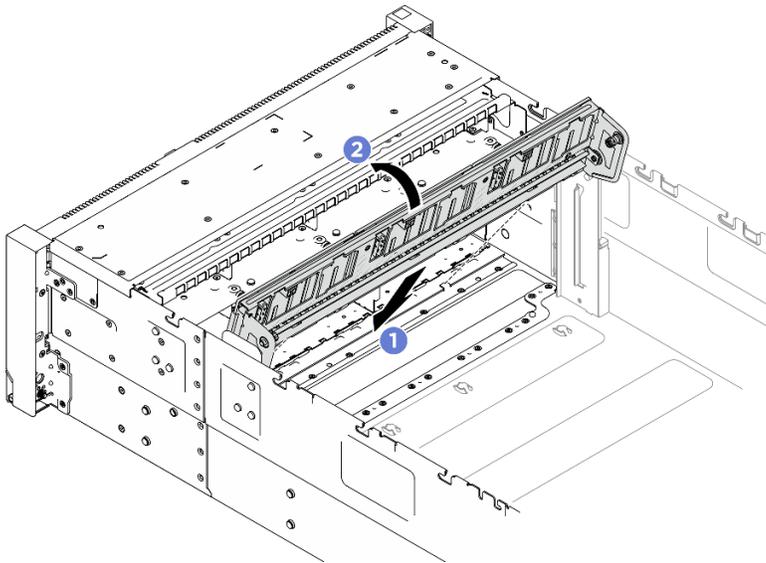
Installation d'un support de fond de panier d'unité (châssis doté d'une baie E3.S)
